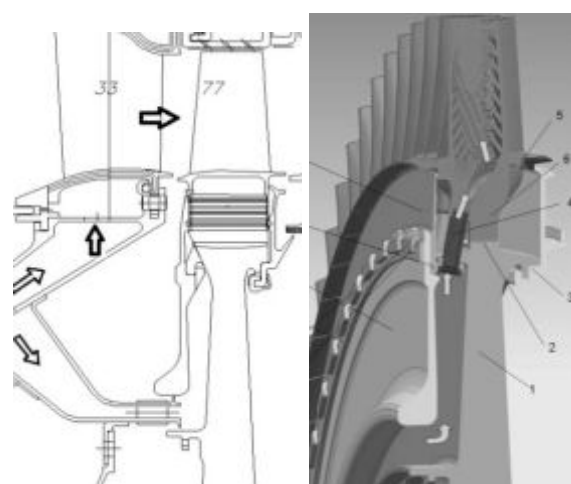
Система подачи охлаждающего воздуха в лопатки замковой конструкции (а) и моноколеса (б)
